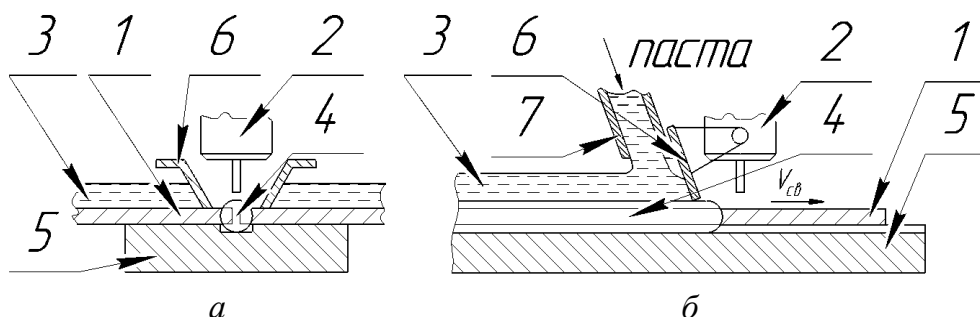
Пример применения теплопоглощающей пасты при сварке: а – предварительное нанесение пасты; б – сопутствующая сварке подача пасты вслед за сварочной головкой; 1 – свариваемые детали; 2 – сварочная головка; 3 – теплопоглощающая паста; 4 – сварочный шов; 5 – подкладка; 6 – защитный экран (а – стационарный; б – подвижный); 7 – выходной патрубок устройства, подающего пасту
